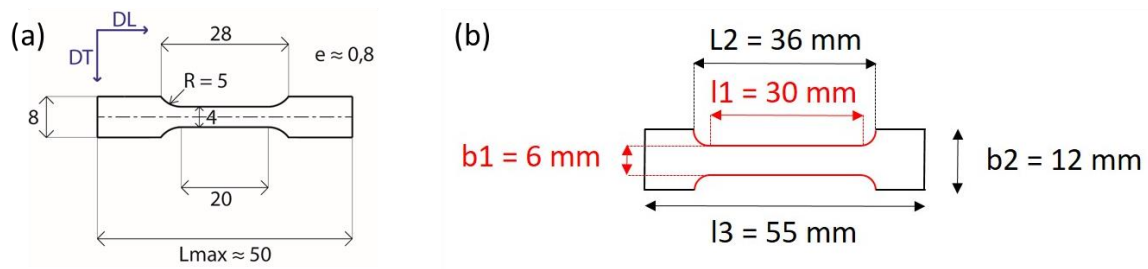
Schéma des éprouvettes de traction pour (a) la machine de 10 kN et (b) la machine de 30 kN
